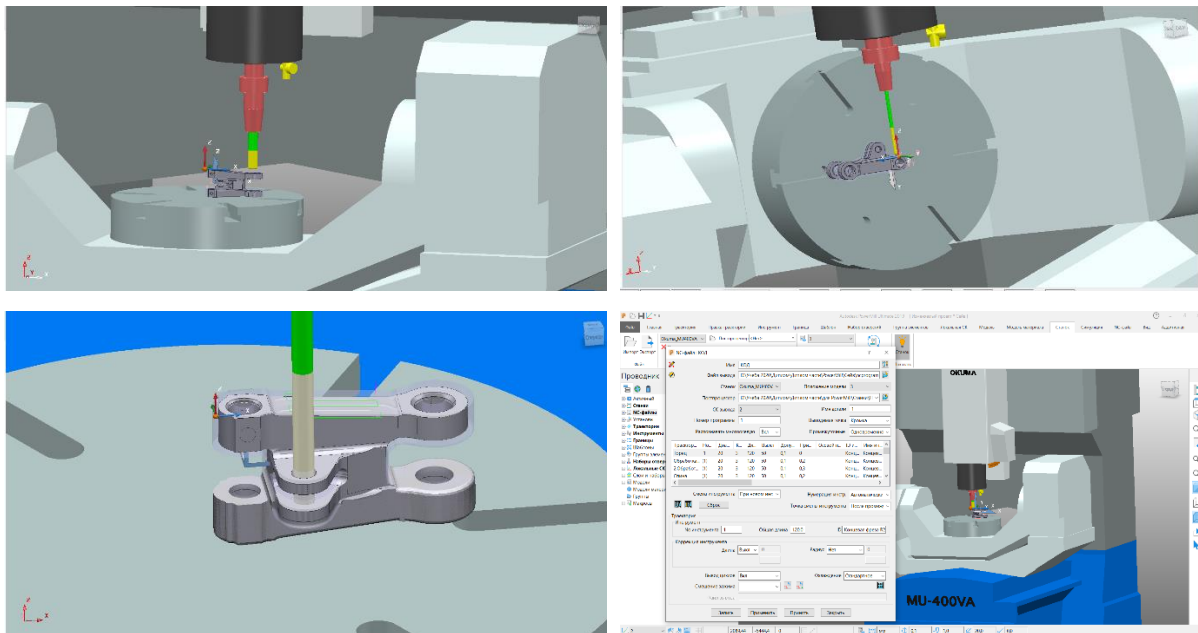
Послідовна механічна обробка деталі Ланка в Autodesk PowerMill
